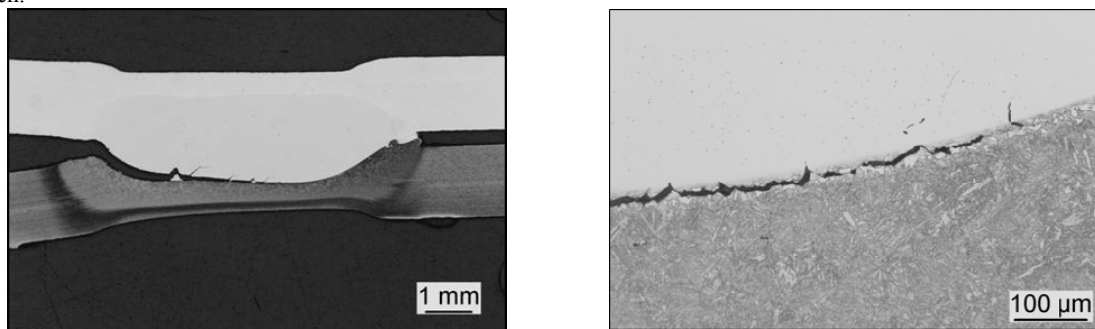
Partieller Dickenbruch entlang der Schmelzlinie zwischen Schweißlinse und WEZ eines TRIP-Stahls einer Mischverbindung an einer unvollständig zerstörten Abrollprobe
